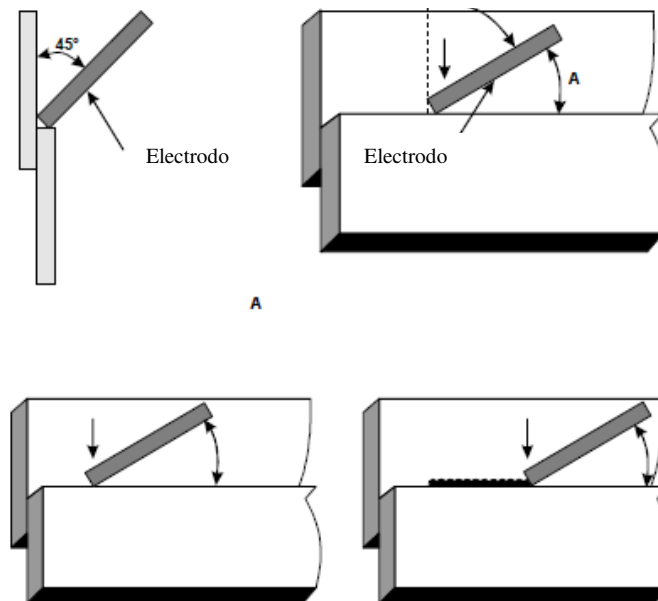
Técnica de autoconsumo para soldadura MMA [7].
